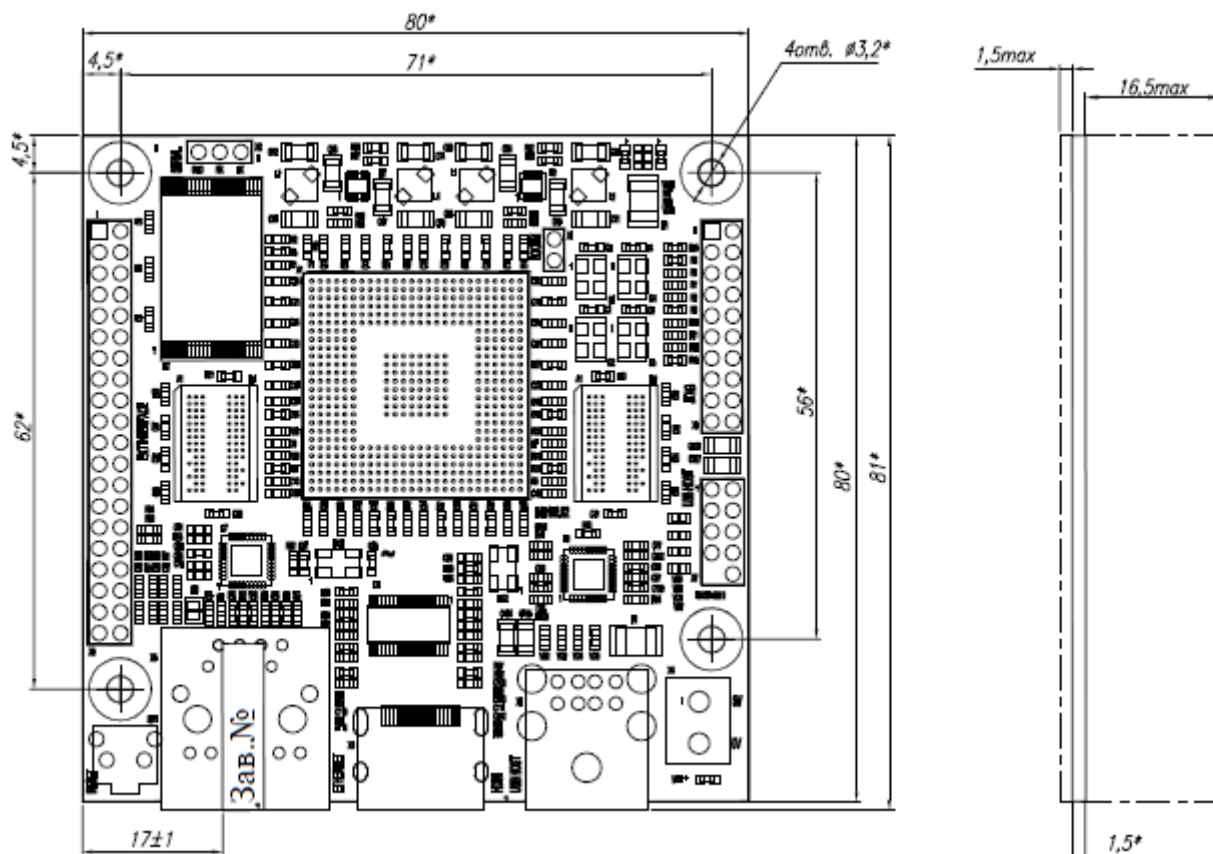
Общий вид модуля МВ106.02, габаритные размеры
